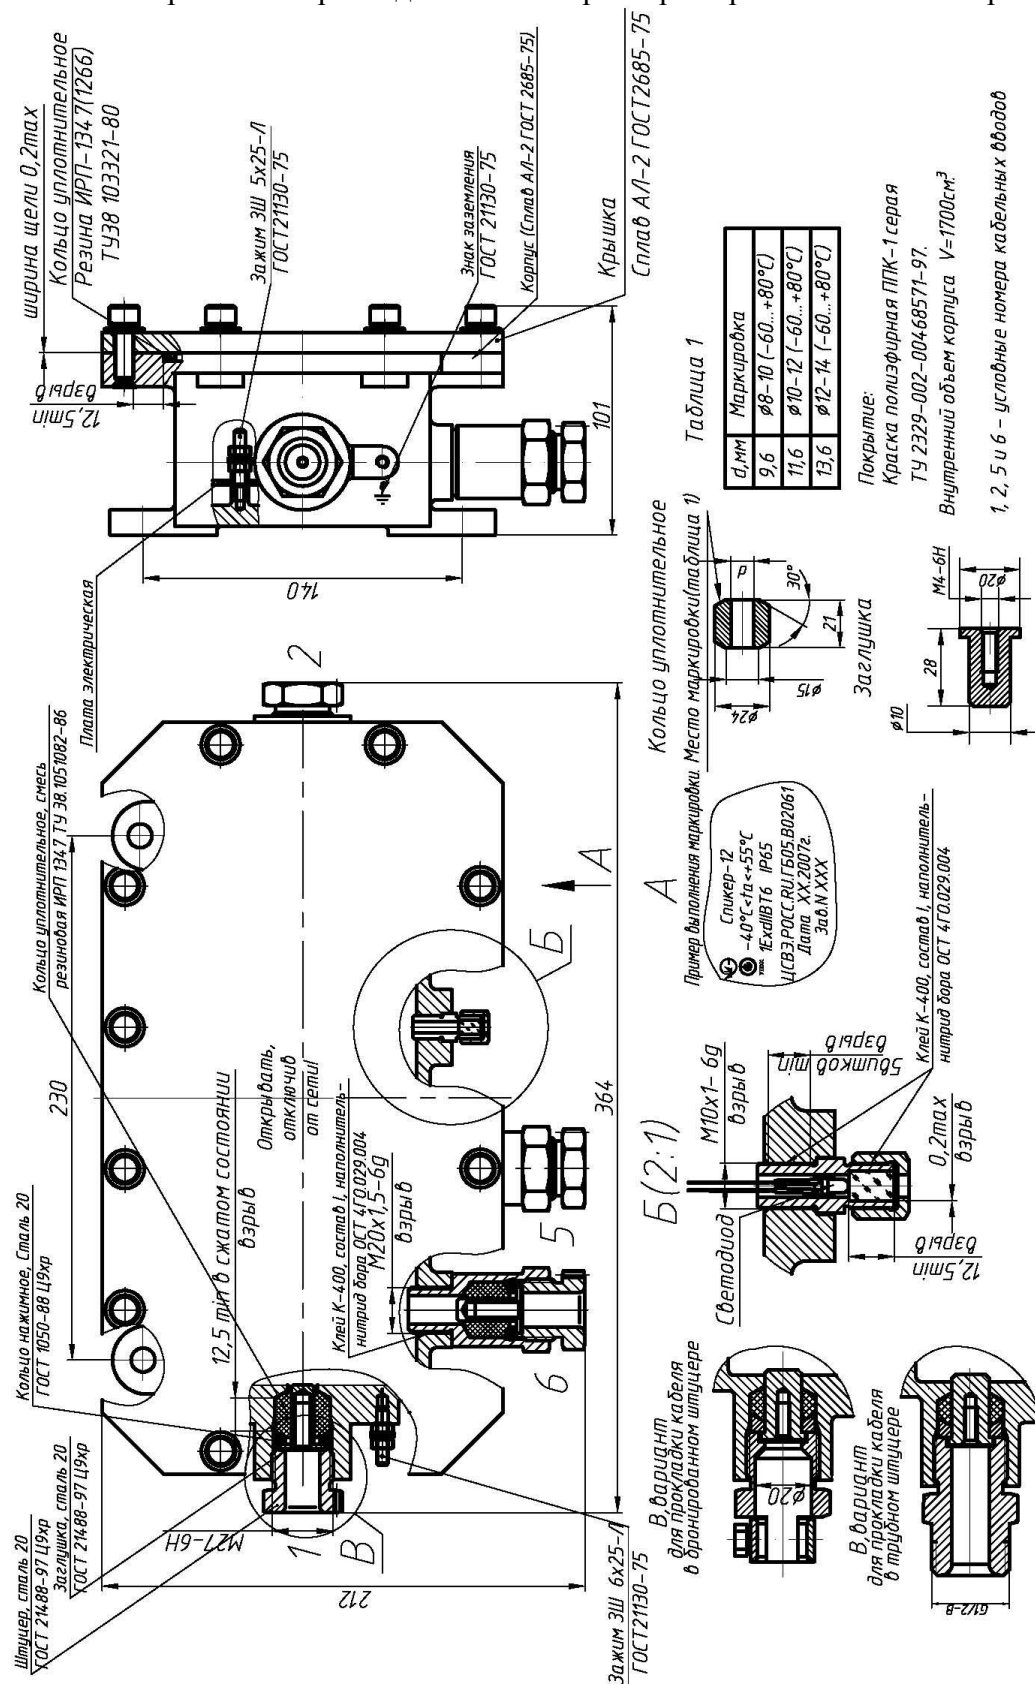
Габаритный чертёж речевого блока Оповещателя СПИКЕР, совмещённый с чертежом средств взрывозащиты
